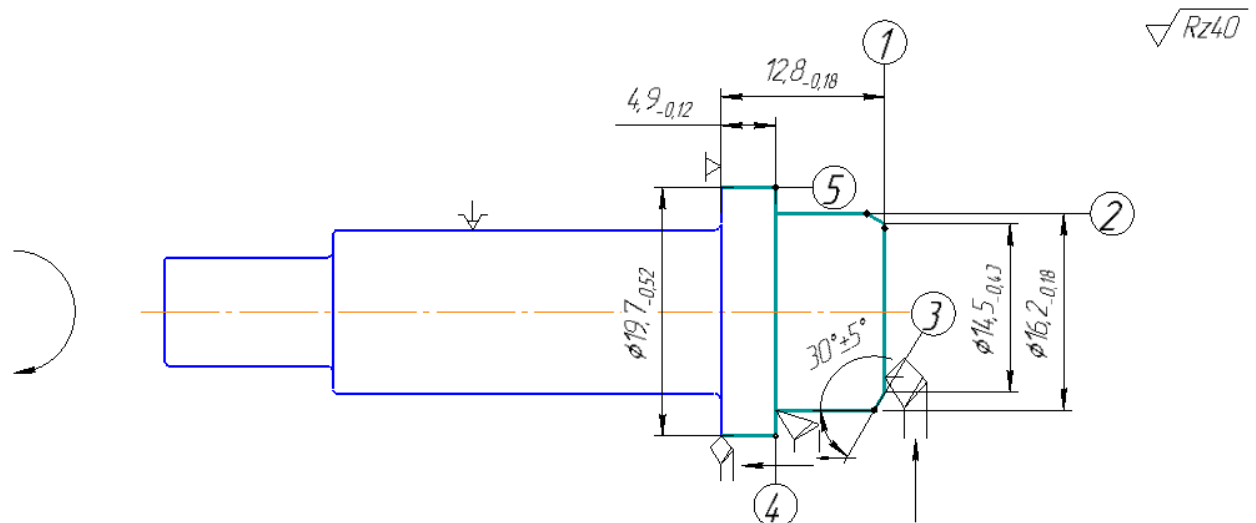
Ескіз обробки на операцію 10 Токарна
